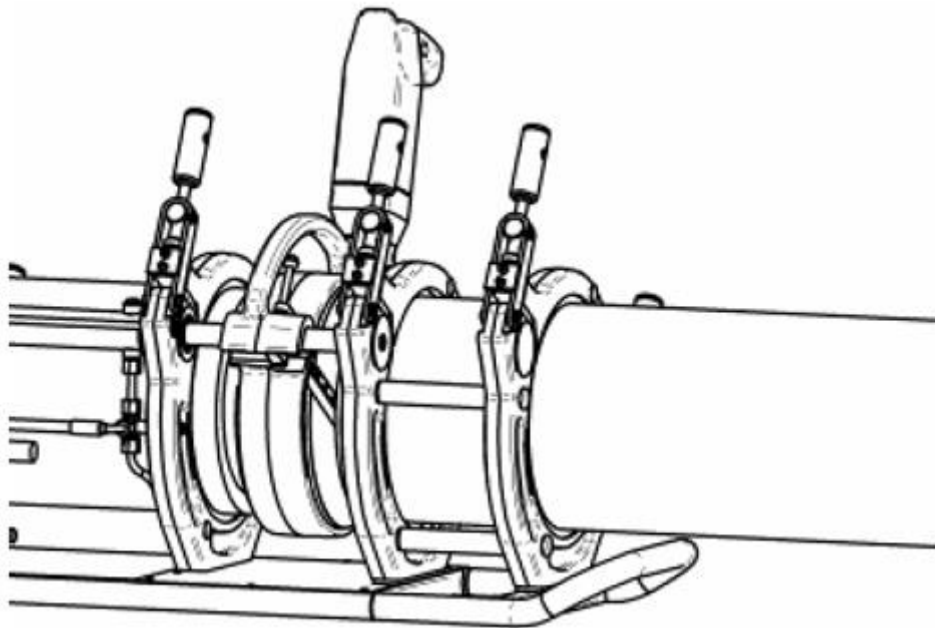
Установка торцевателя между свариваемыми торцами труб
